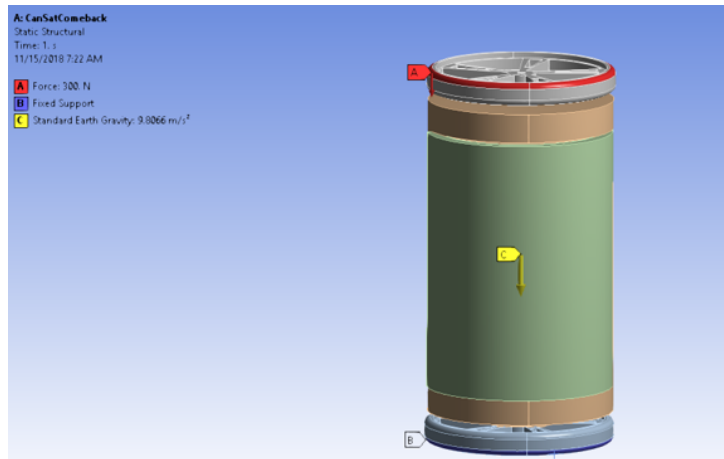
Fuerzas y restricciones aplicadas a la estructura del CanSat.
